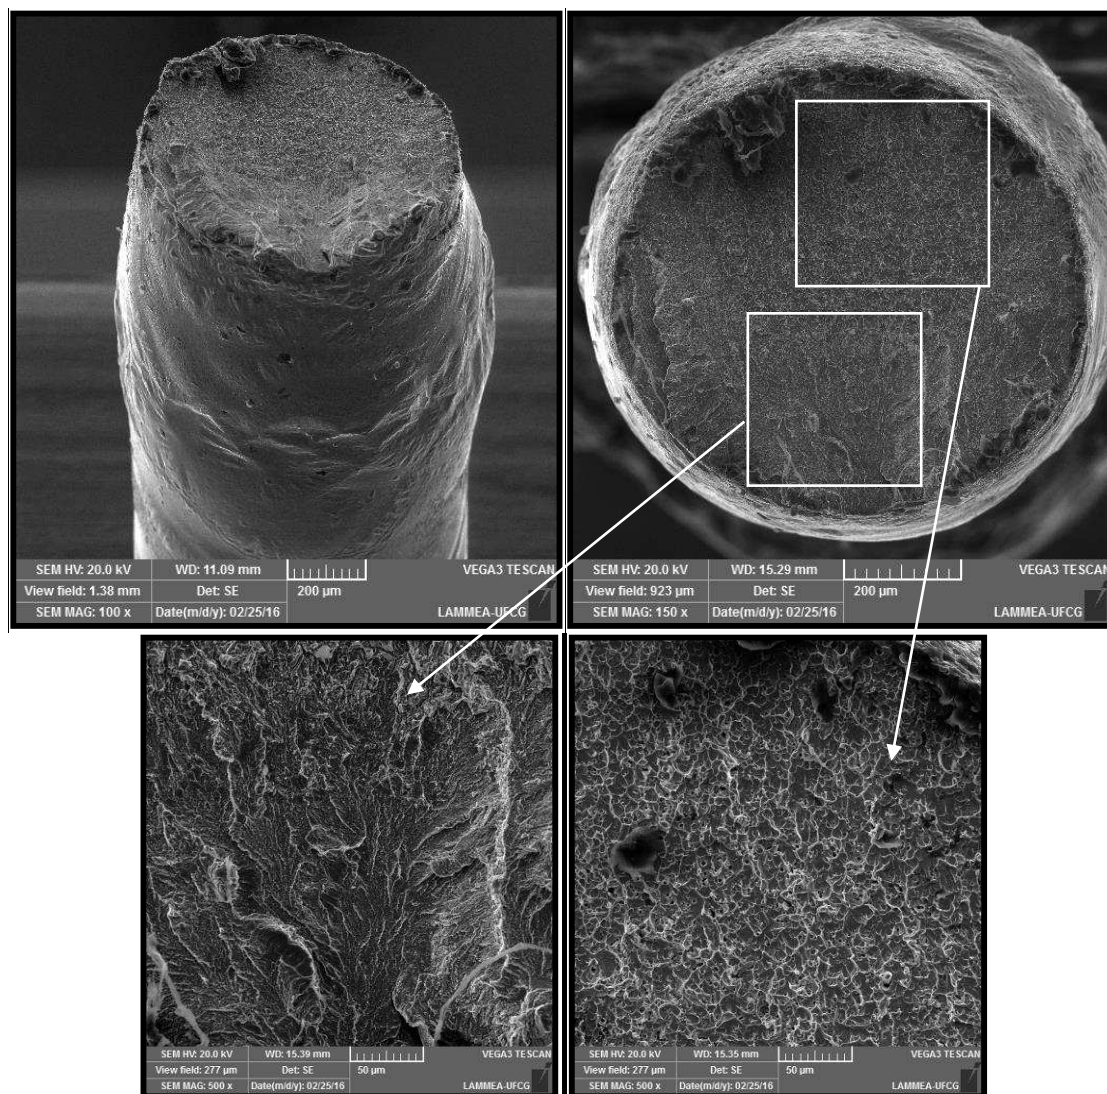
Superfície de fratura da junta dissimilar soldada na configuração 7ms/70% e submetido a ruptura a 90°C.
